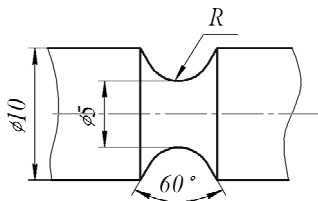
Образец из стали 38Х2МЮА с надрезом радиуса R
